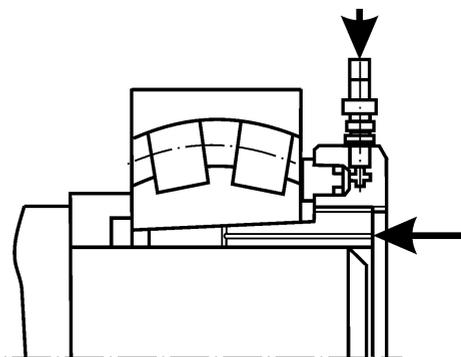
Разборка подшипников со стяжной втулкой с применением гидравлической гайки и подводом масла на сопряженные поверхности подшипника и втулки
